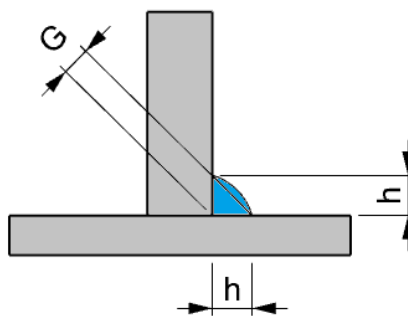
Garganta y pie de soldadura en T.
